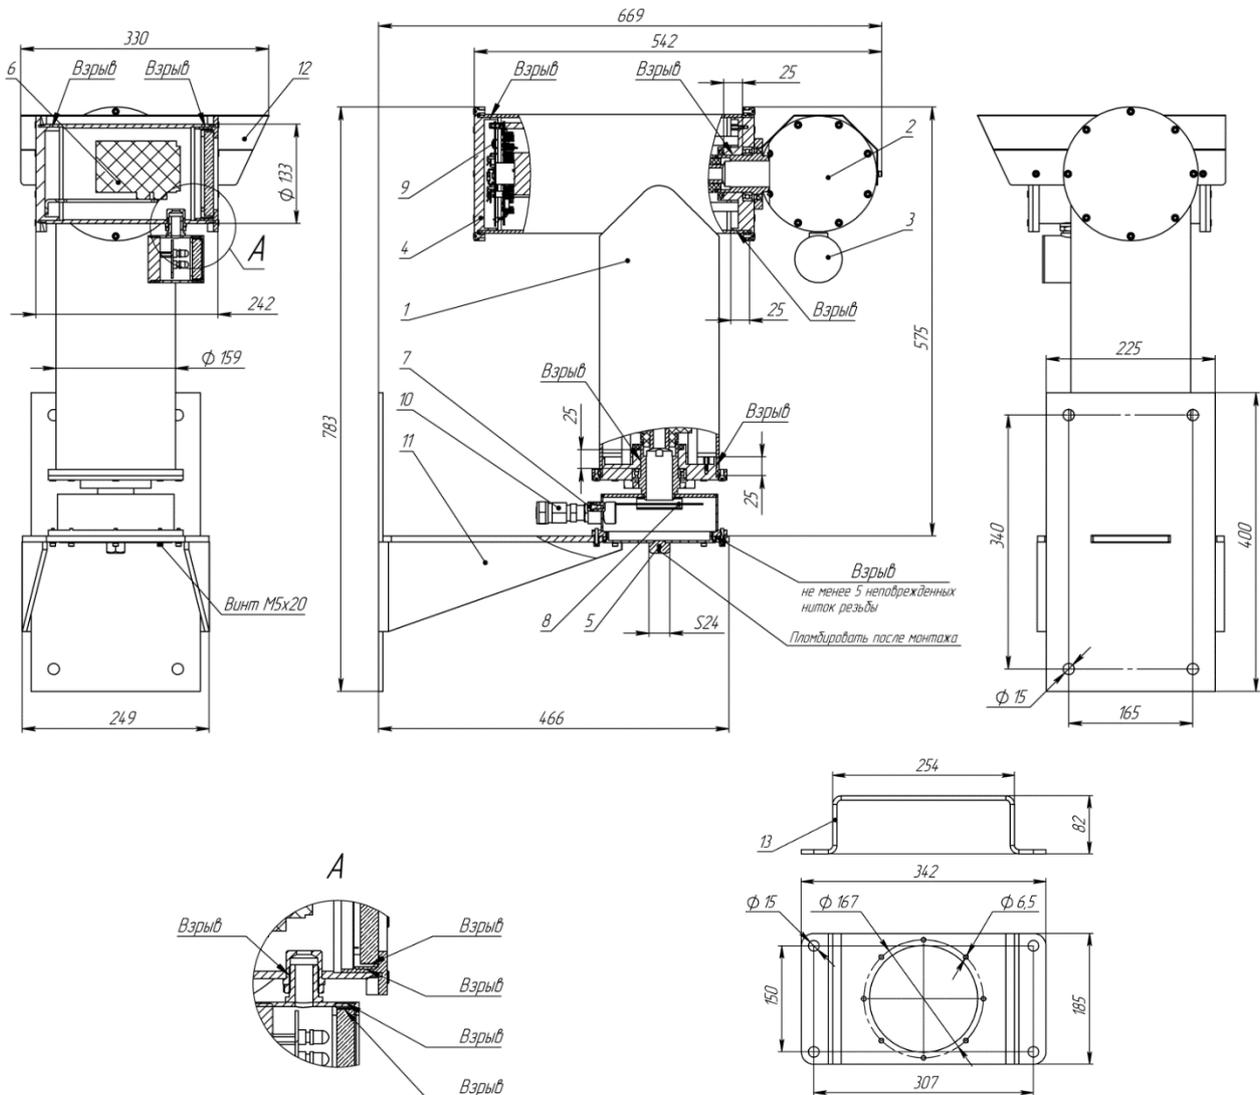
Внешний вид и размеры TOP-07e-LTV-Ex
